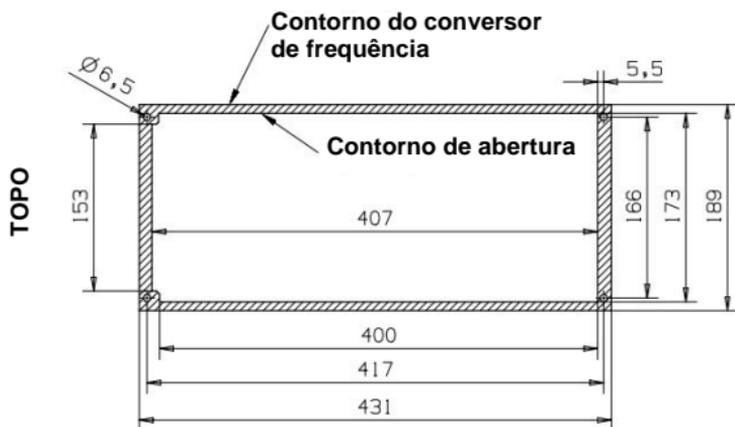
Dimensões do recorte para montagem em flange do M15
